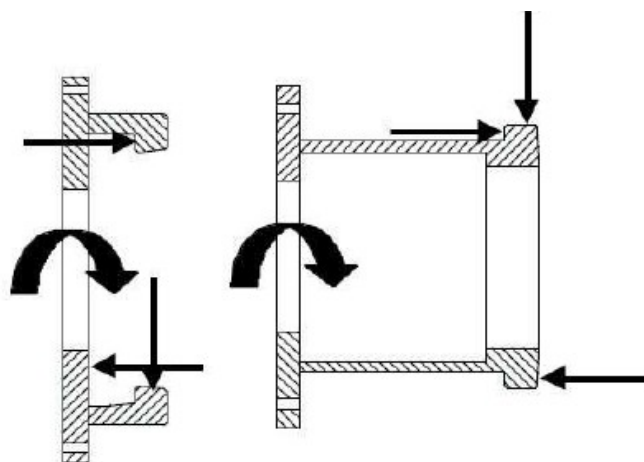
Нагрузки охватывающей (слева) и охватываемой (справа)
